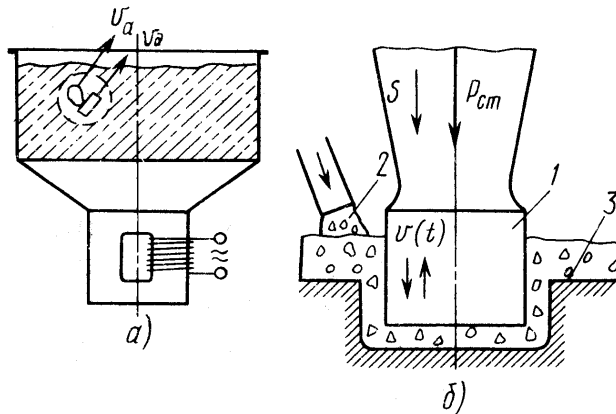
Ультразвуковий спосіб механічної обробки [12]
